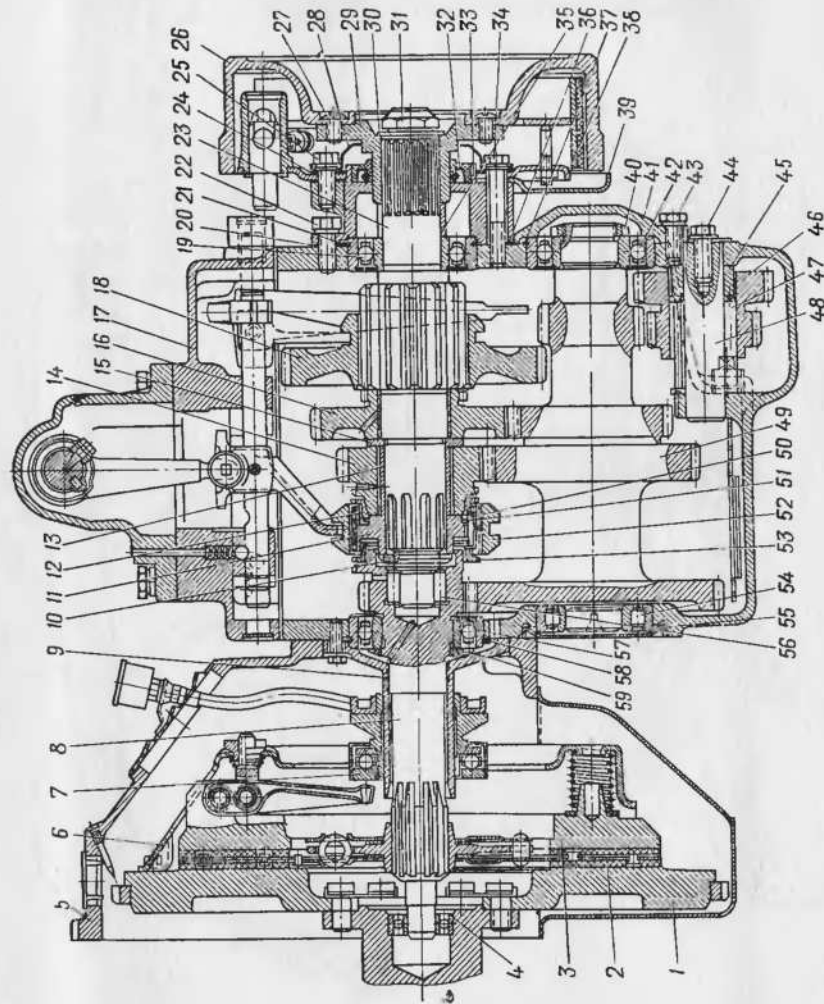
Коробка передач с центральным тормозом и сцеплением:
